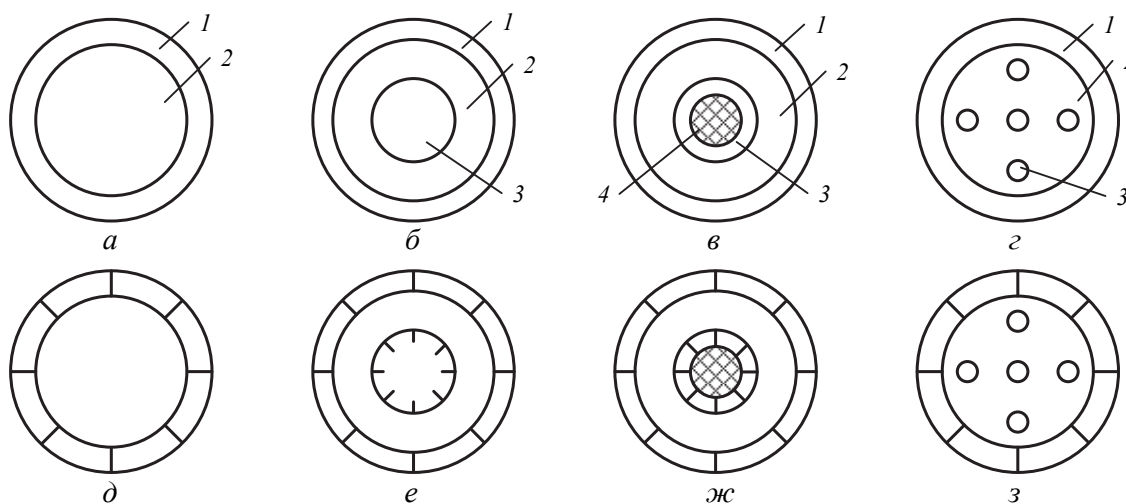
Схемы конструкций воздухоподогревателей с гладкими (*a–г*) и оребренными (*д–ж*) каналами:
